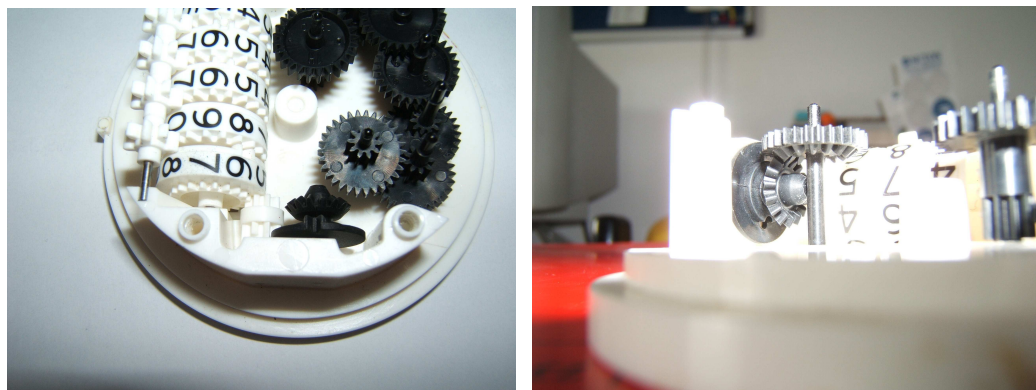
Mecanism cu angrenaj cu roți dințate conice
